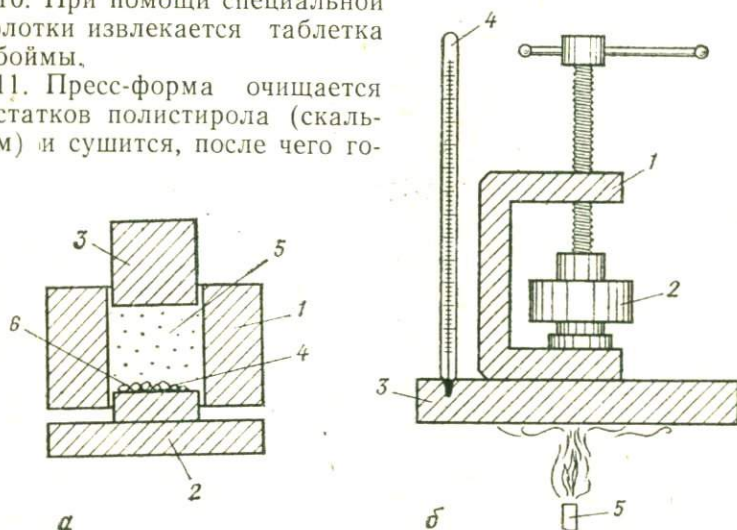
Приспособление для изготовления таблеток из полистирола для микронного анализа: а — разрез пресс-формы, 1 — корпус пресс-формы, 2 — нижний пуансон, 3 — верхний пуансон, 4 — зерна минералов, 5 — полистирол, 6 — полированная поверхность пуансона; б — изготовление таблетки: 1 — струбцина-пресс, 2 — снаряженная пресс-форма, 3 — массивная стальная плита, 4 — термометр, 5 — газовая горелка
